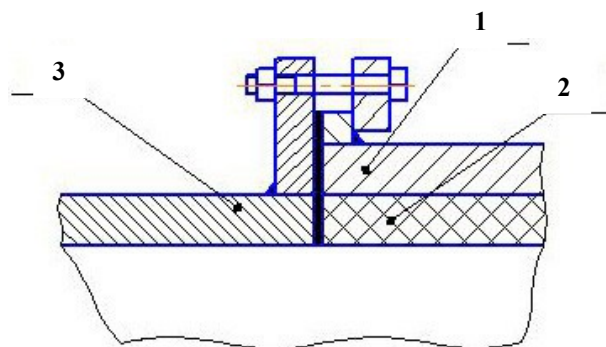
Вариант присоединения трубы с керамическим покрытием к трубе без покрытия.
